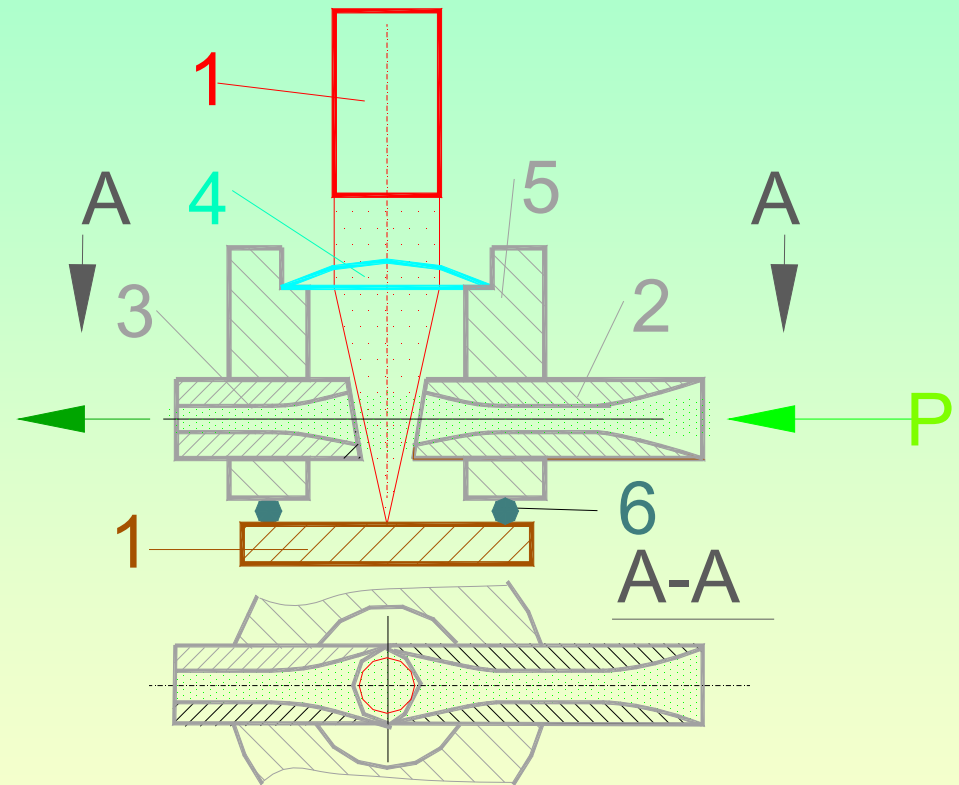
Схема доопрацювання порожнини лазерним променем під час обробки
